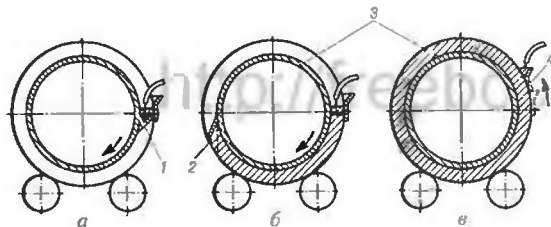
Схема електрошлакового зварювання кільцевих швів;
